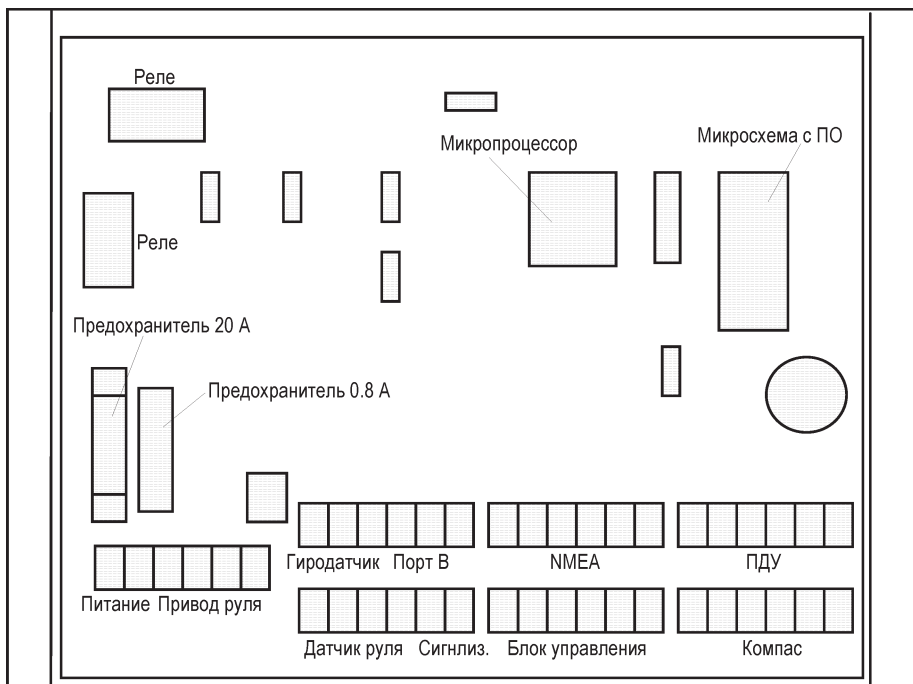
Расположение деталей и разъемов блока курсового процессора CM840
